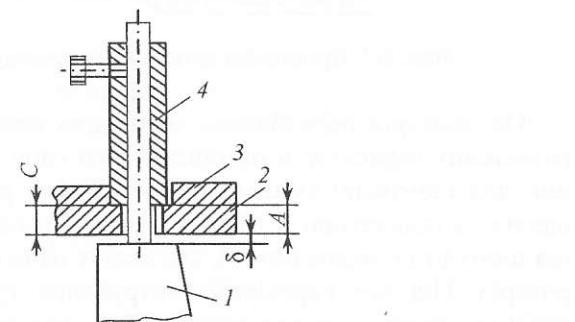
Схема заміру зазору між корпусом основного компресора і робочими лопатками:
